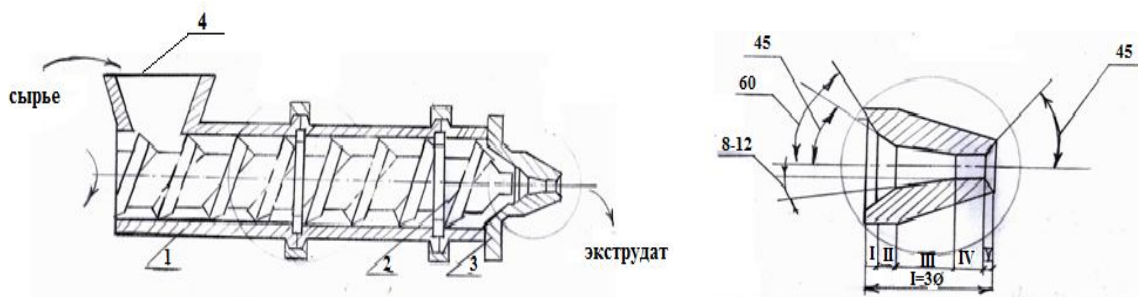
а) общий вид устройства для экструдирования кормосмеси 1-корпус; 2-винт; 3-фильера; 4 загрузочная камера; б) конструктивно технологическая схема матрицы экструдера
